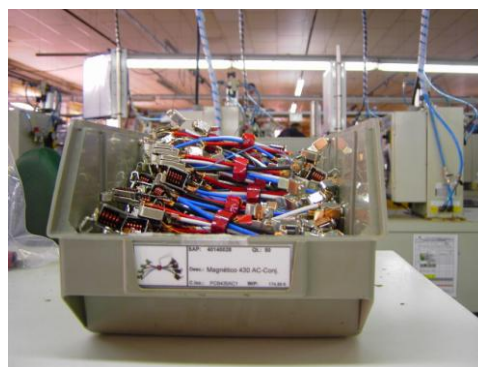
\_ exemplo de um contentor das soldaduras
